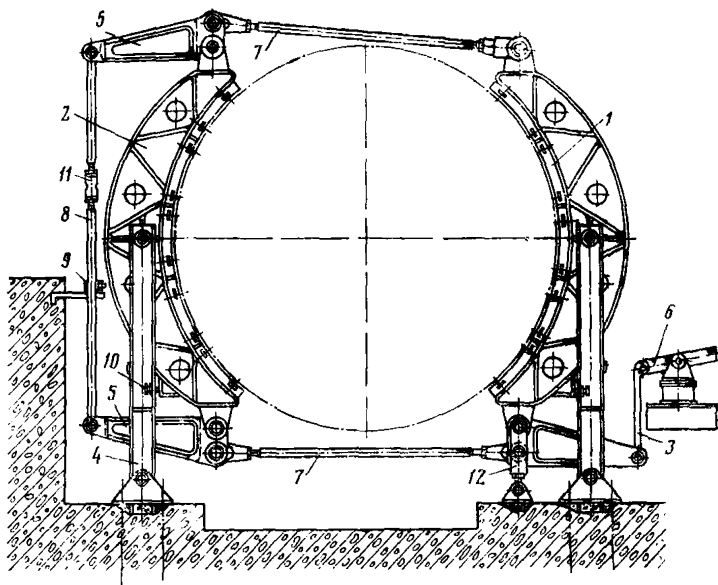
Исполнительный орган тормоза с комбинированным перемещением колодок:
